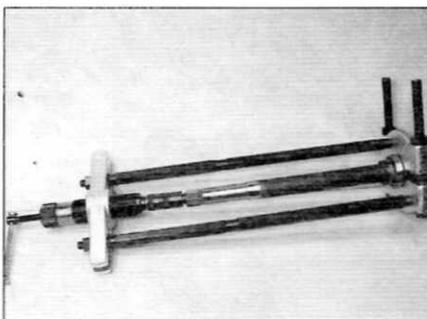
Используя длинный съемник подшипников, снимите промежуточный подшипник с правой полуоси
